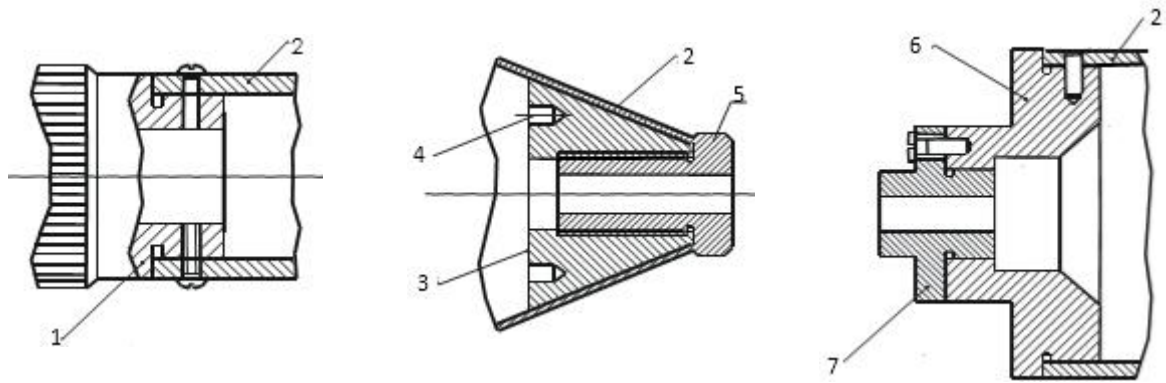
Конструкції круглих корпусів: 1 – об'єктивний вузол; 2 – тонкостінний трубчастий корпус (для запобігання від деформації труба насунута на тверду частину корпуса об'єктивного вузла); 3 – клин; 4 – отвір для інструмента (при нагвинчуванні клина на трубчасту частину клин починає розсовувати трубчастий корпус, забезпечуючи надійне кріплення за рахунок сил тертя); 5 – циліндрична частина(в ній можна встановити оптичну систему); 6 – твердий корпус (виконує сполучення тонкостінного трубчастого корпуса великого діаметра з тубусним фланцевим елементом малого діаметра. Твердий корпус захищає від деформацій тонкостінний трубчастий корпус і виконує с функції сполучення для тубусного елемента); 7 –тубусний фланцевий елемент
